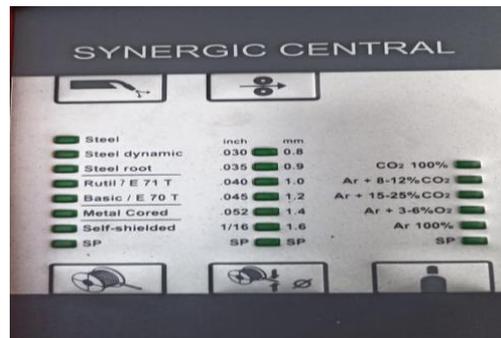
Panel frontal de la soldadora Fronius 2700
